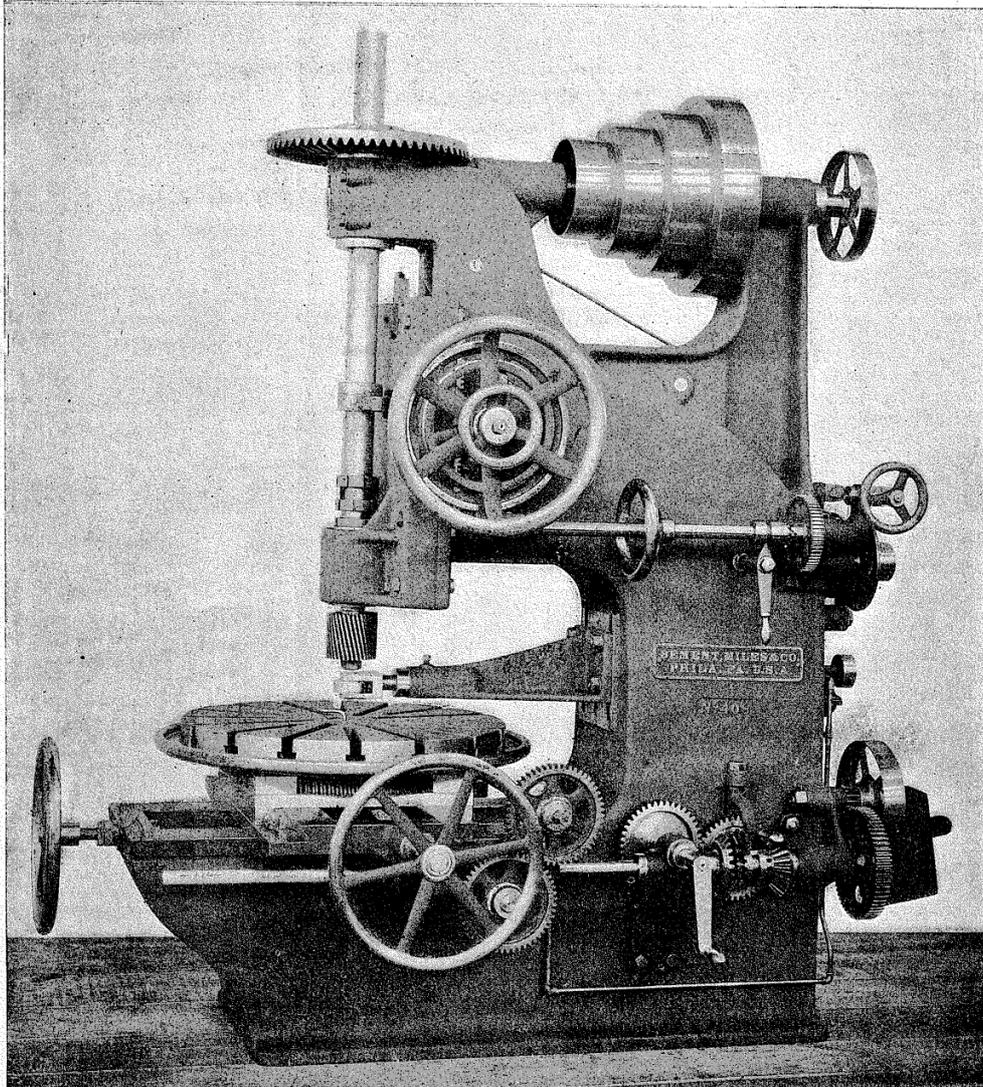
Fraiseuse verticale *Bément Miles* genre *Desgranchamps* (G. Richard, *Traité des machines-outils*, vol. II, p. 34). Broche de 82 millimètres, course 430, équilibré, distance à la colonne 668, du plateau au bras 400, avances réversibles instantanément et vitesse, graduation à continue, chariot compound se déplaçant de 660 × 710 transversalement; plateau de 810 millimètres de diamètre.
